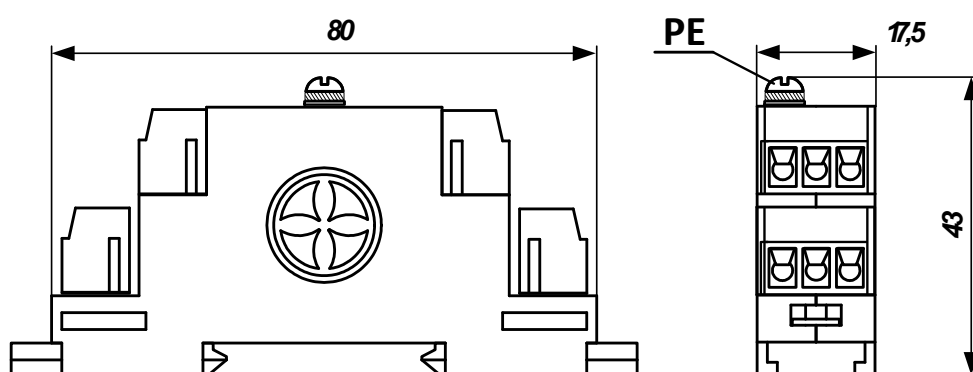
Габаритные размеры устройства Commeng DIP
